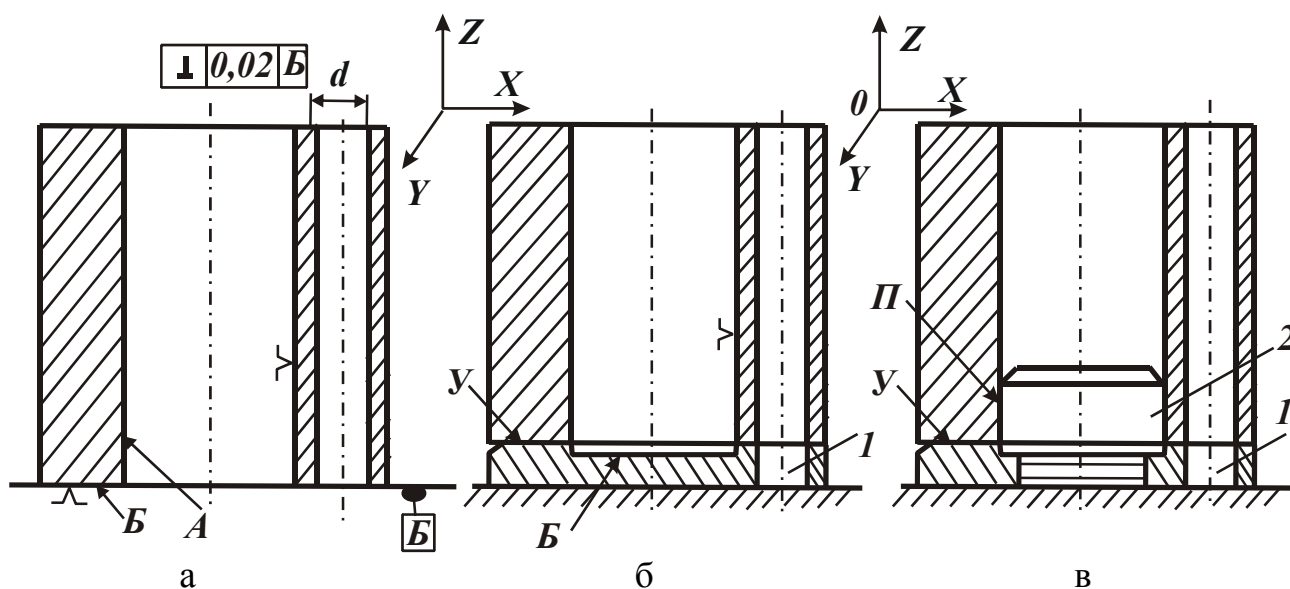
Неправильное базирование заготовки двумя базами.
